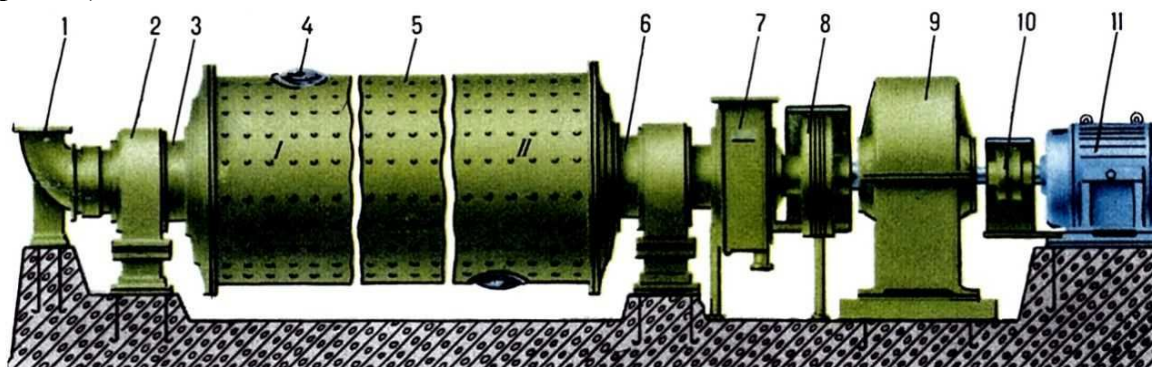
Мельница барабанная: I-II – камеры помола; 1 – загрузочная воронка; 2 – роликовая опора; 3 – загрузочная часть; 4 – люк; 5 – барабан мельницы; 6 – разгрузочная часть; 7 – кожух разгрузки; 8 – эластичная муфта; 9 – редуктор; 10 – пальцевая муфта; 11 – электродвигатель
